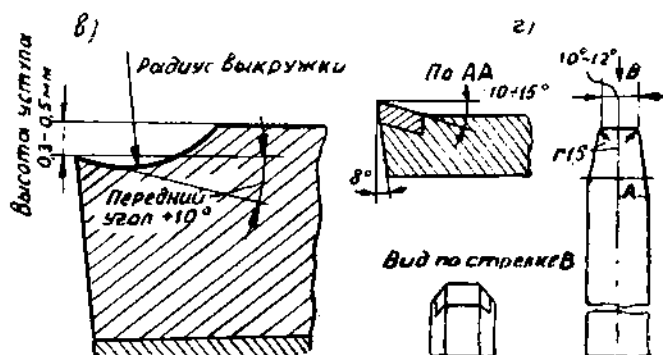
в — резец для чистового точения твердых сталей (выкружка с порогом);
